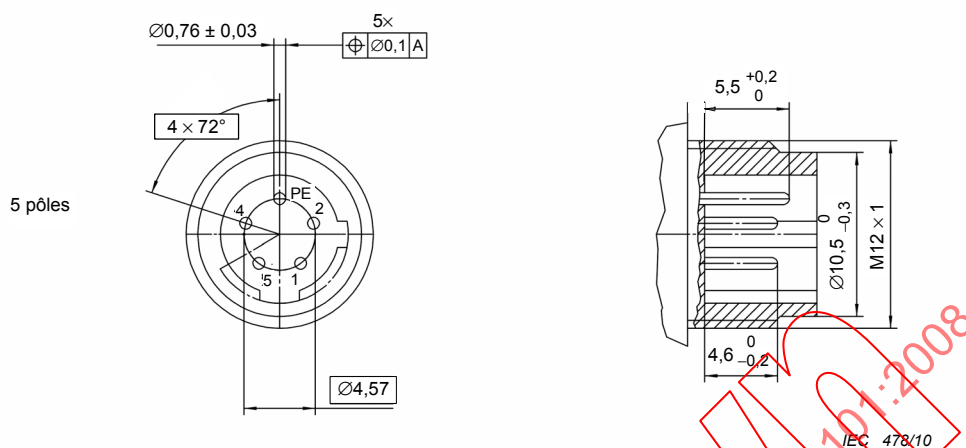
Vue de face du contact mâle, 5 pôles, codage C
